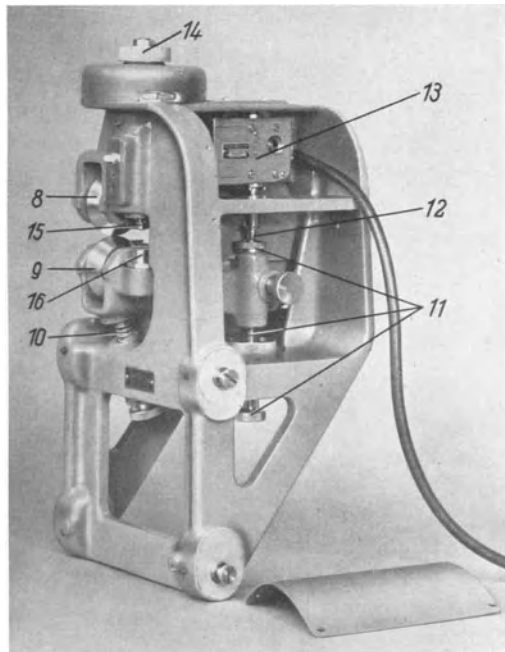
Abtasteinrichtung für Blechdickenmesser.
